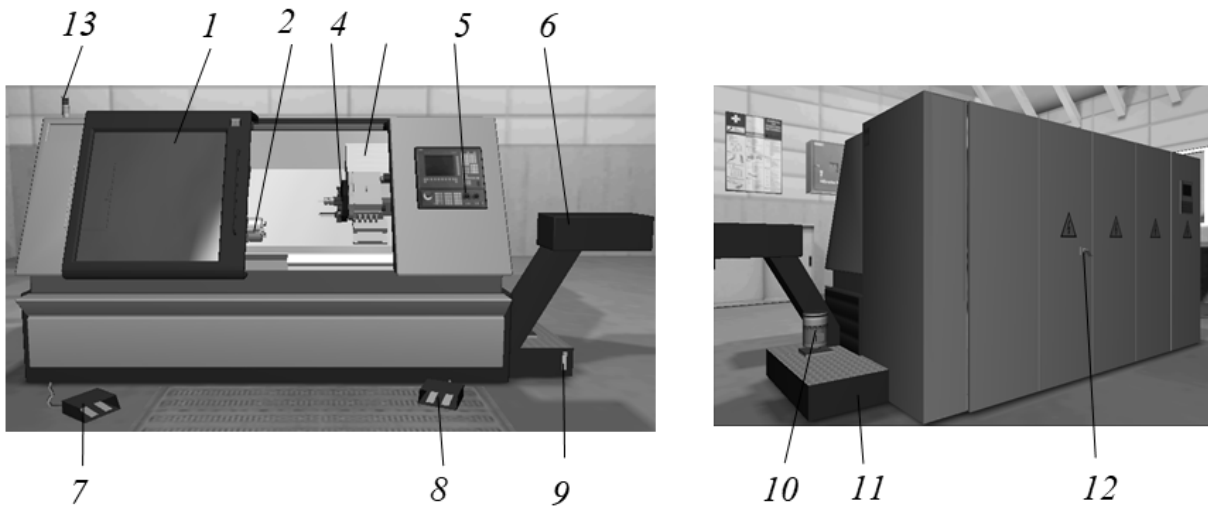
Основные элементы конструкции токарного станка с ЧПУ
